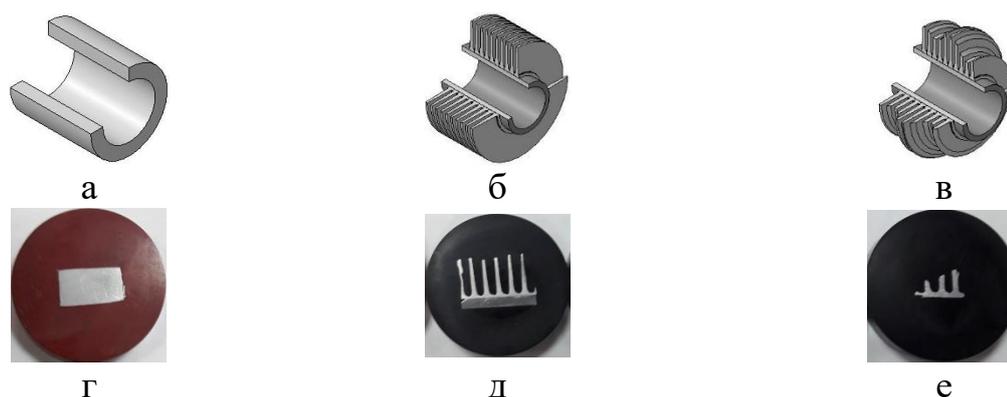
Экспериментальный образец алюминиевой трубы: а) алюминиевая заготовка; б) ребристая труба; в) бракованная ребристая труба; г) шлиф, вырезанный из алюминиевой заготовки; д) шлиф, вырезанный из ребристой трубы; е) шлиф, вырезанный из бракованной ребристой трубы
